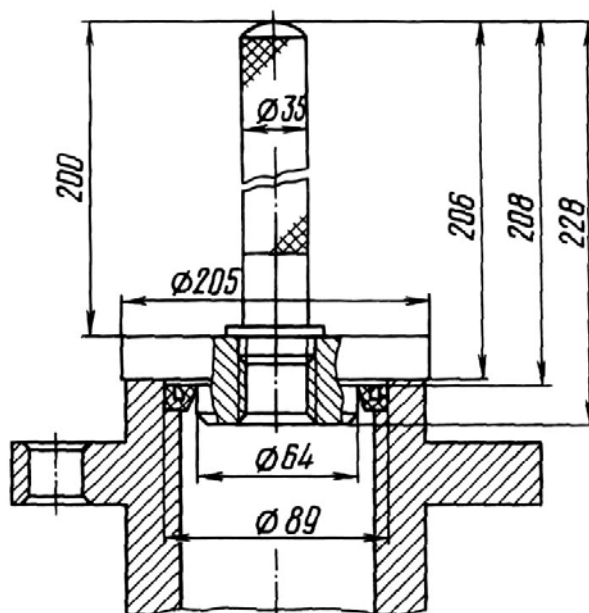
Запрессовка манжеты в корпус шаровой опоры
